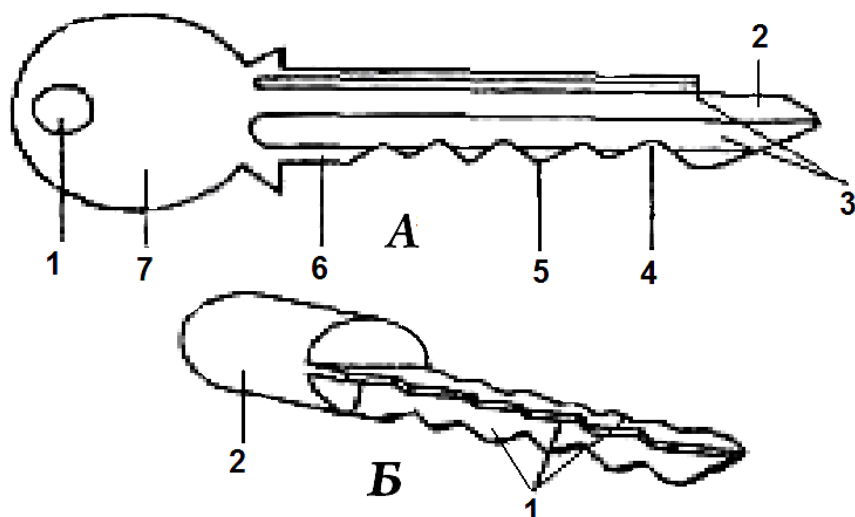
Ключи для замка с цилиндрическим механизмом:
